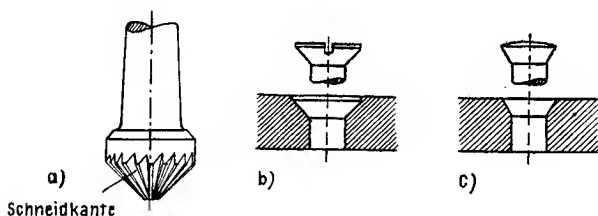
Zum Versenken benutzt man den Spitzsenker (a); richtige Senkung für Senkschraube (b) und Senkniet (c)
